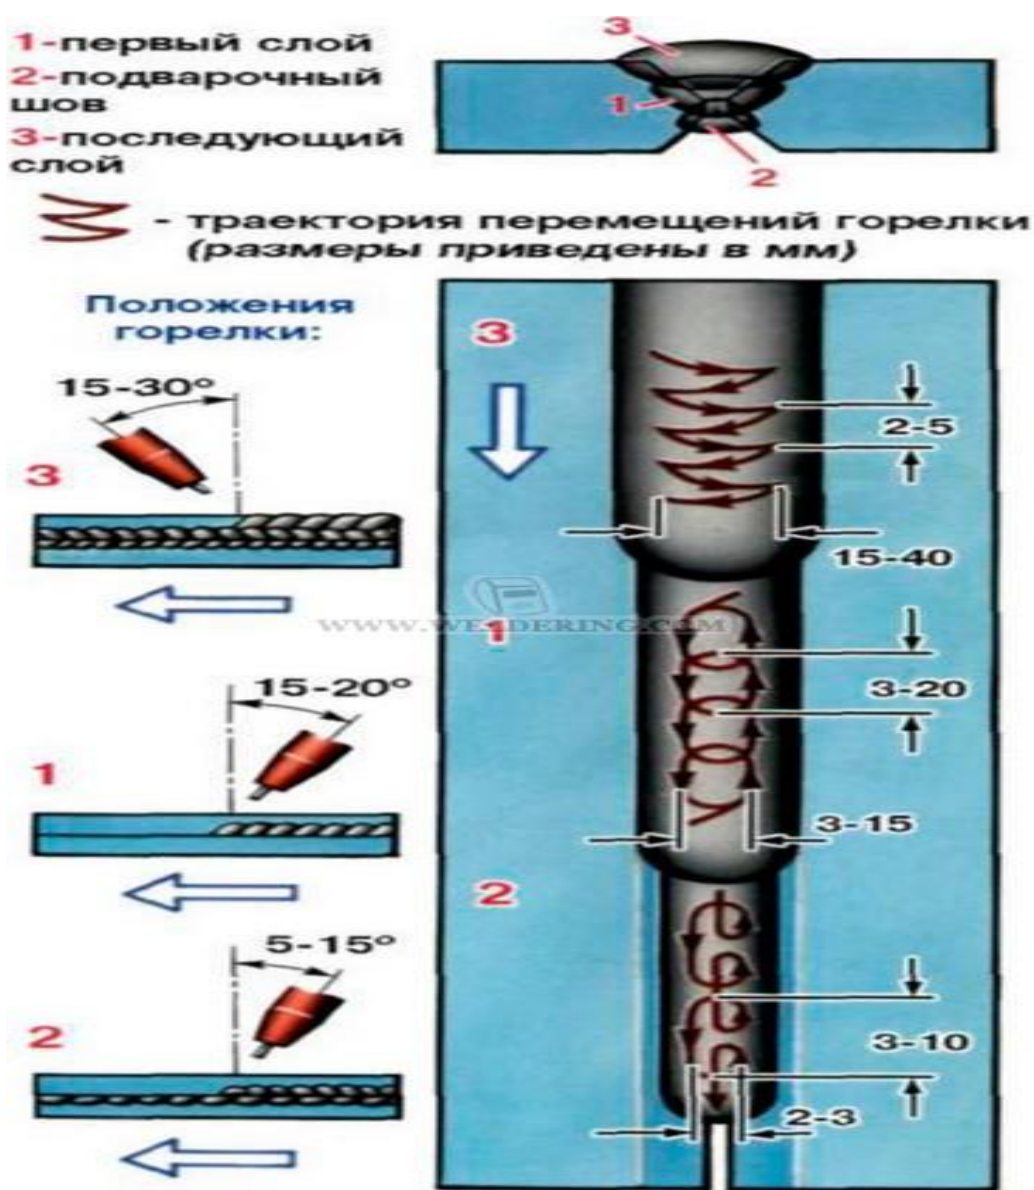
Влияние положение горелки и техники выполнения сварных швов на формирование сварного шва
